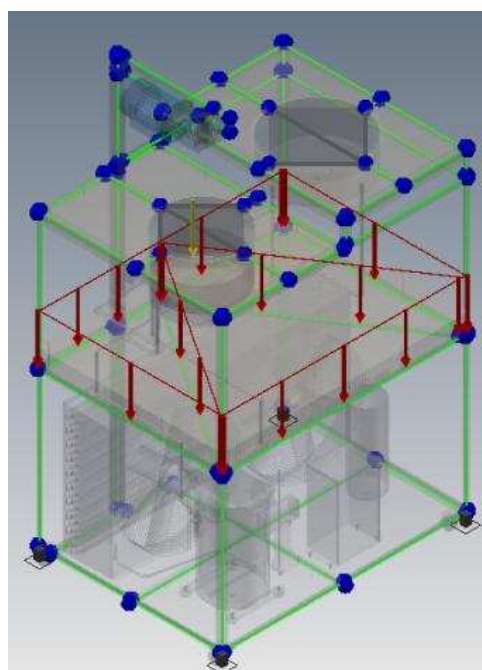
Cargas distribuidas producidas por el aislante y planchas de acero bajo los contenedores de la mezcla.
